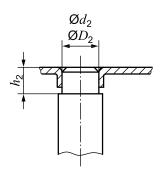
Dimensions d'ajustement de la roue des minutes et de l'aiguille des minutes
